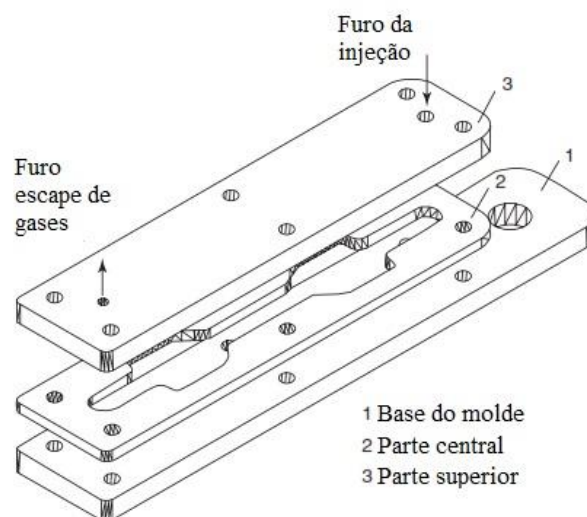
Vista explodida de um molde destinado à produção de provetes por injeção [20]
